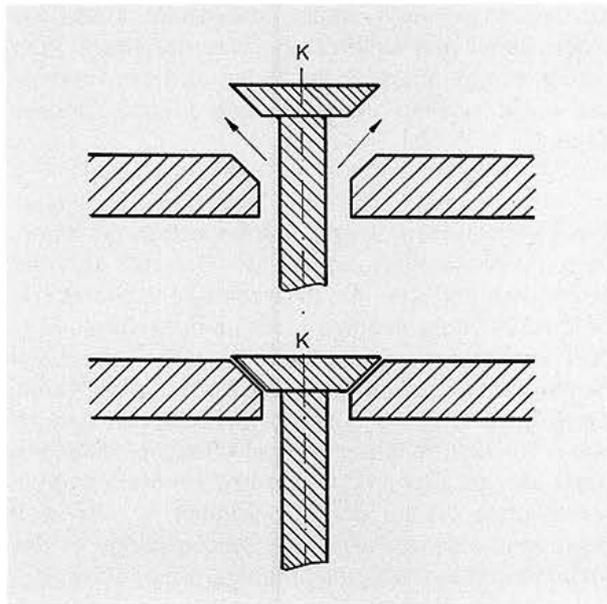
Kegelventil, oben geöffnet, unten geschlossen:
